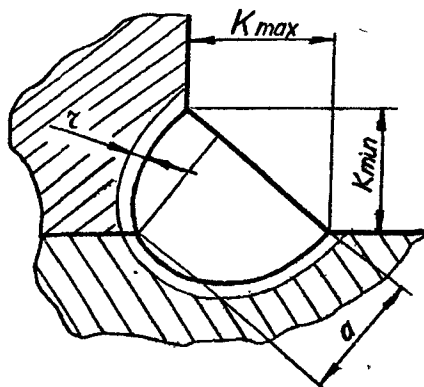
Форма сечения углового шва после фрезеровки его торца
